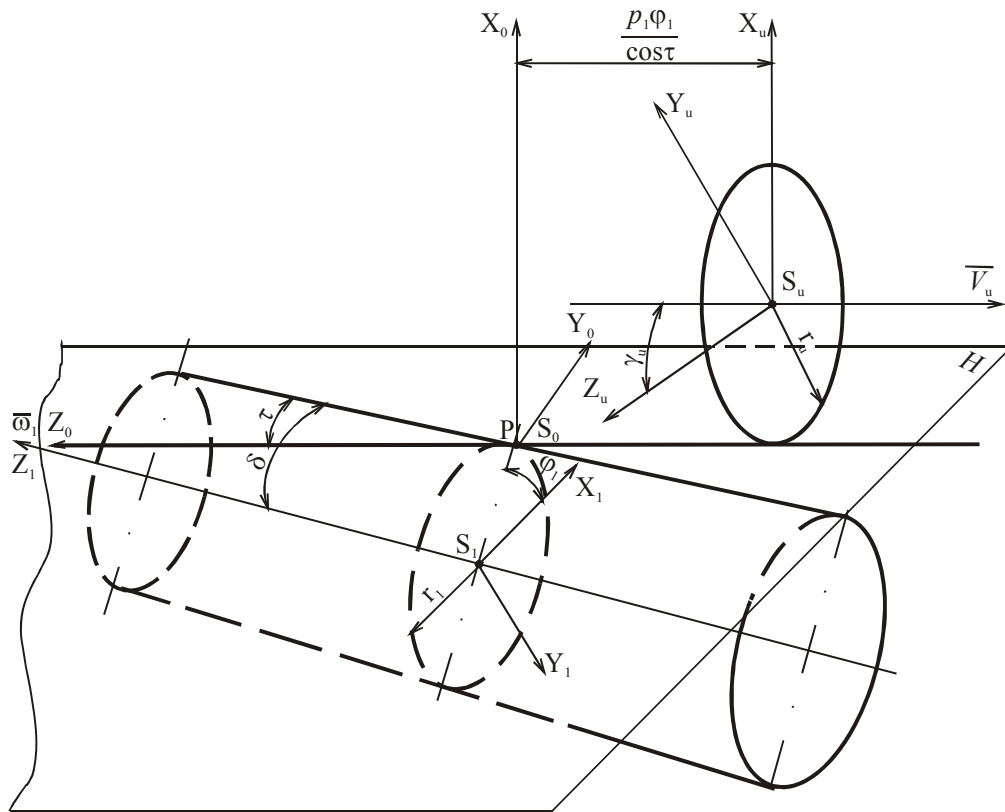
Верстатне зачеплення для нарізання витків конічного черв'яка дисковим інструментом [5]
